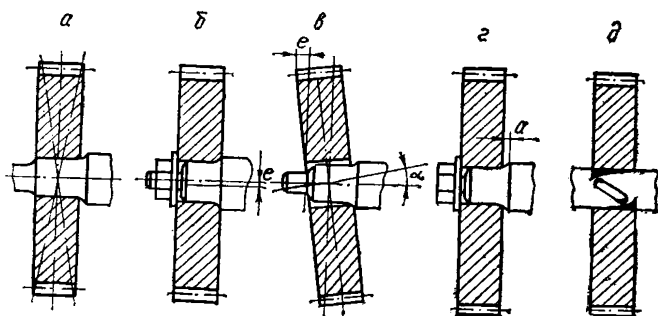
Погрешности установки зубчатых колес на валу:
